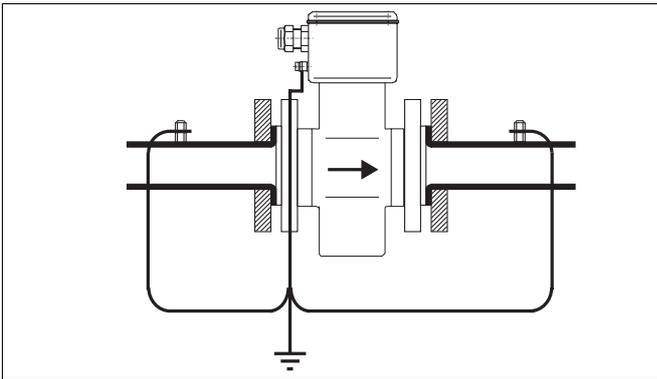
Aufnehmer DN 3 bis 40, Schraubflansch
